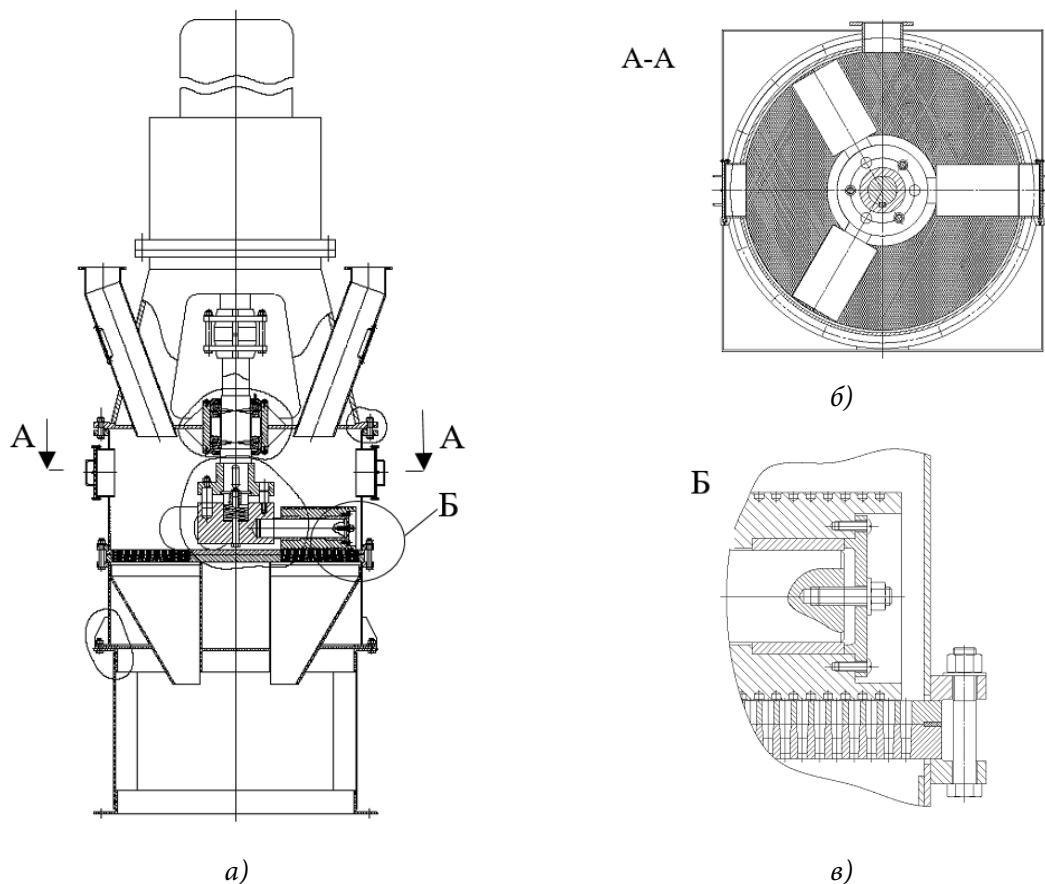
Схема роторного гранулятора с плоской матрицей: а) общий вид гранулятора; б) узел размещения прокатывающих роликов над матрицей; в) конструкция крепления плоской матрицы в корпусе
